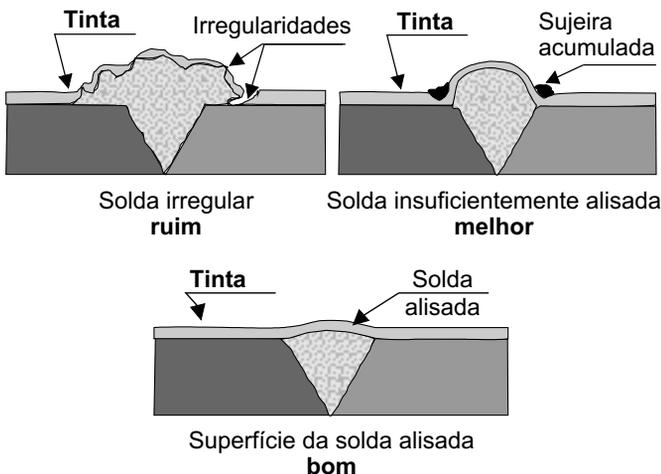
A superfície da solda deve ser analisada para diminuir a possibilidade de corrosão
